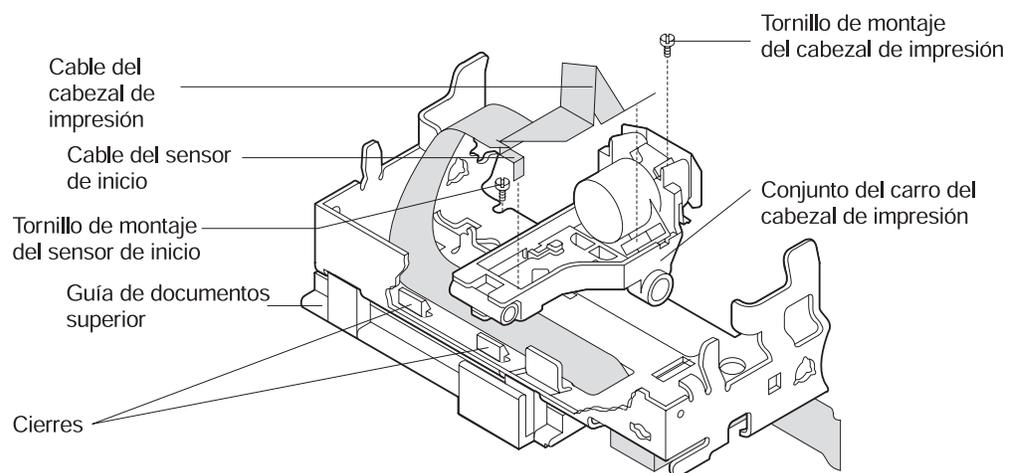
Extracción del cable del cabezal de impresión/sensor de inicio
